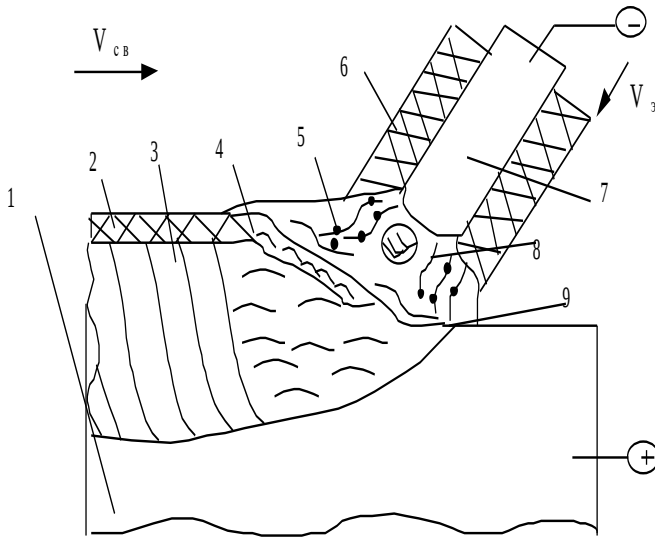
Схема формирования сварочной ванны (4+9) при сварке покрытым электродом
